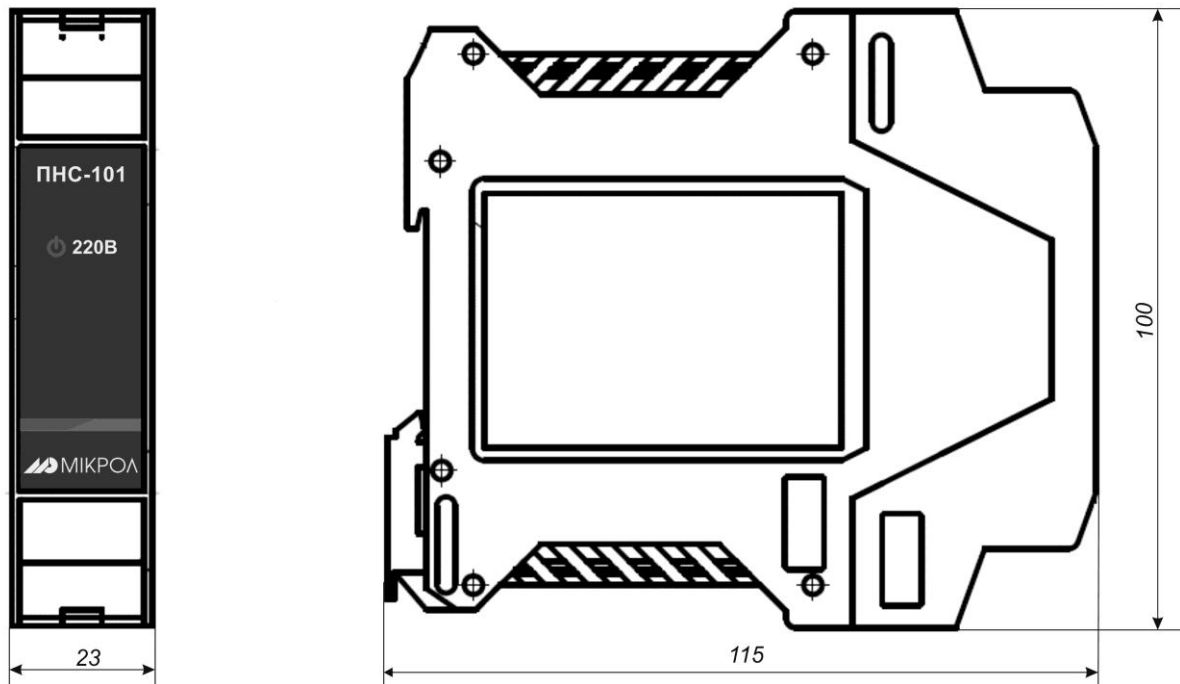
Внешний вид и габаритные размеры ПНС-101
